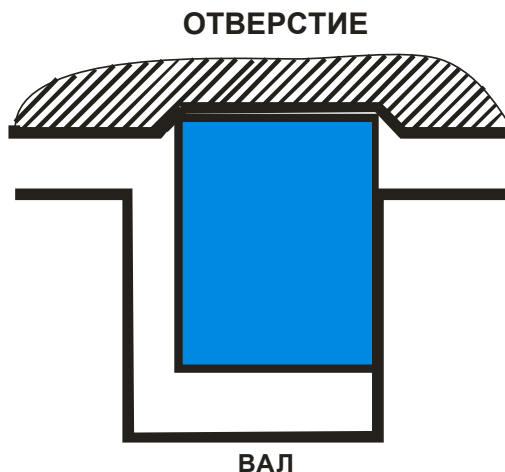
Характерный износ боковой стенки канавки, самого кольца и цилиндрической поверхности отверстия
